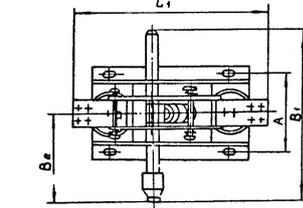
Разъединитель трехполюсный типоразмера РВЗ 10/400-630-1000 I, II, III УХЛ2, РВЗ 11/630-1000 I, II
